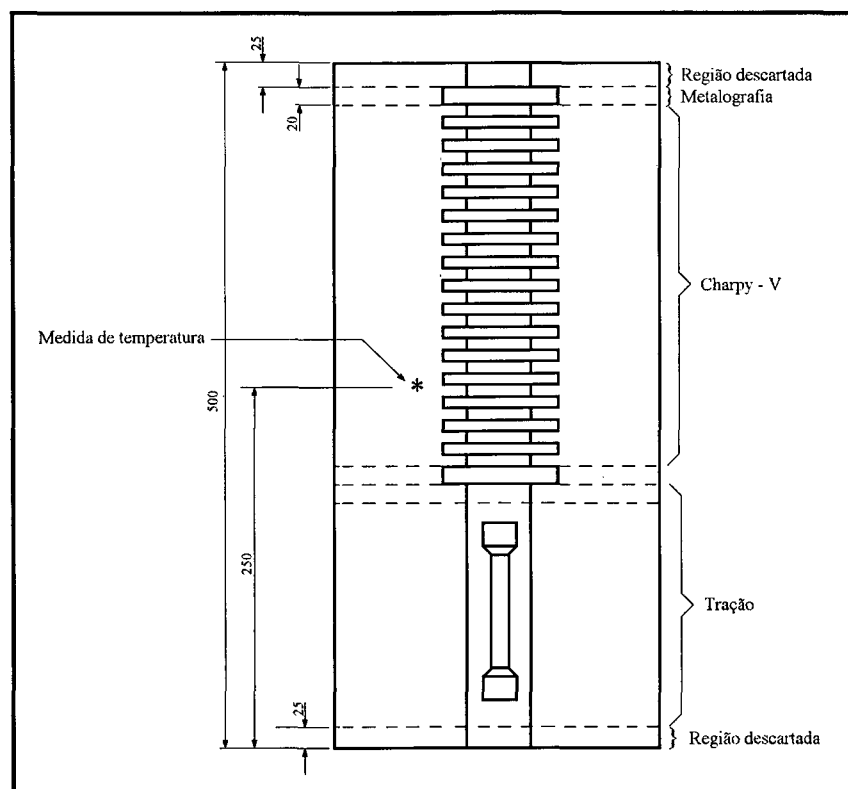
Layout para a retirada de amostras do metal de solda. Soldagem semi-automática. Dimensões em mm.
